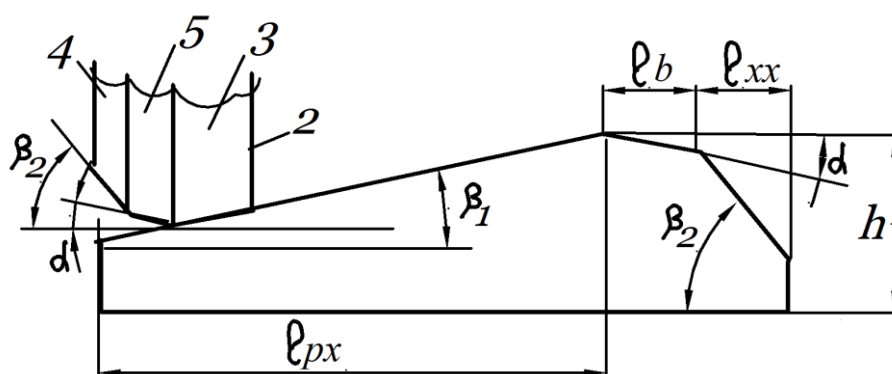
Схема контакта поверхностей кулачково-винтового механизма
